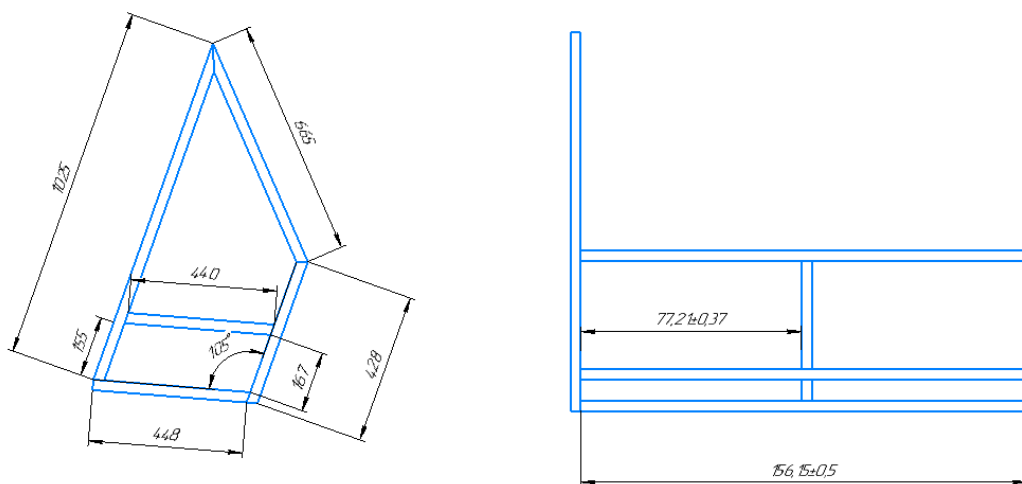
Чертеж сидения разрабатываемой конструкции
